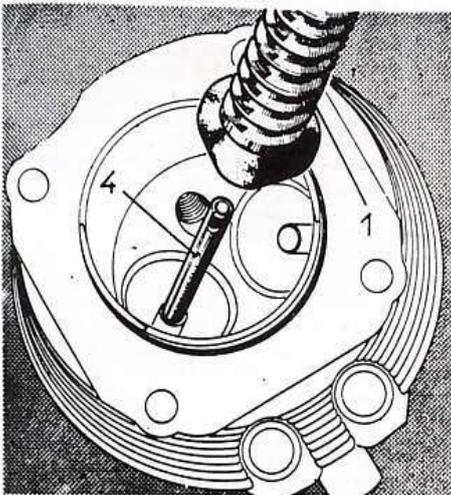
Rectification d'un siège de soupape. 1. Meule - 4. Guide pilote.
